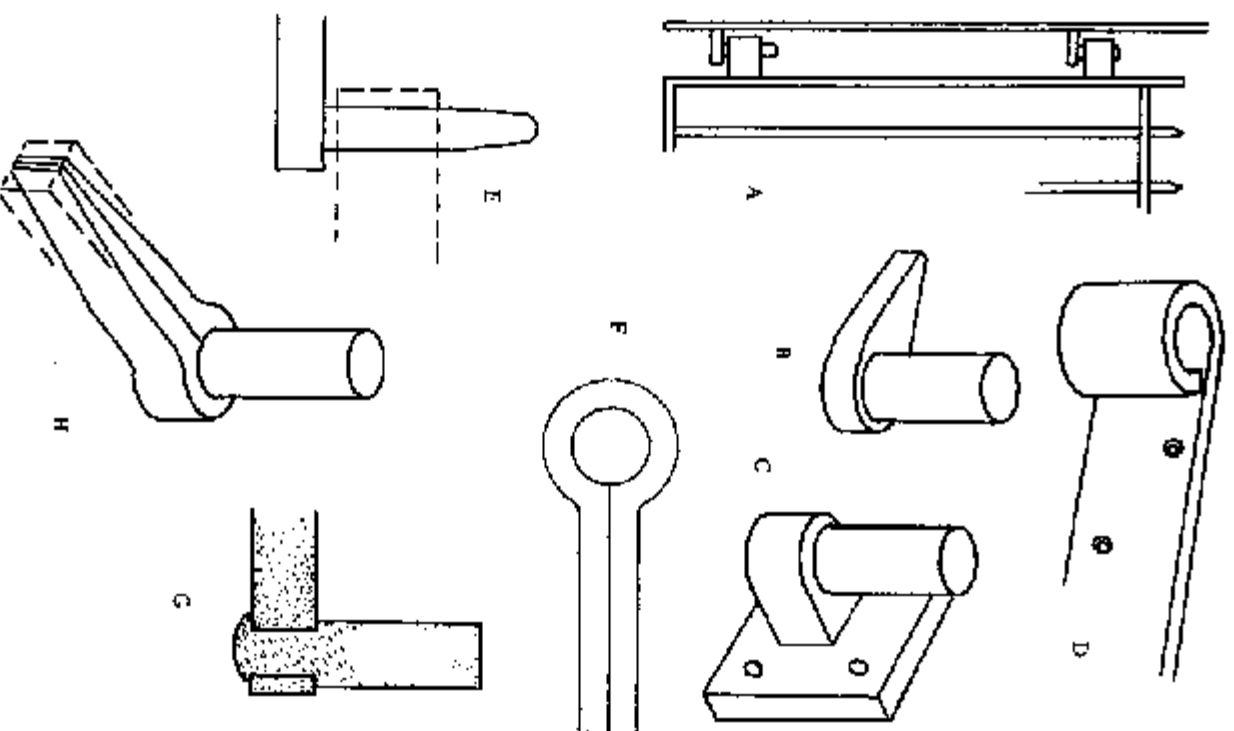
Las bisagras pueden girar sobre sus machos: (A) reja de hierro forjado; (B) reja para el campo; (C) soldado a la placa; (D) bisagra de tira; (E) abrase y redondearse la punta; (F) tira soldada; (G) Machuelo soldado y re-anchado; (H) se ensalza con la punta.
